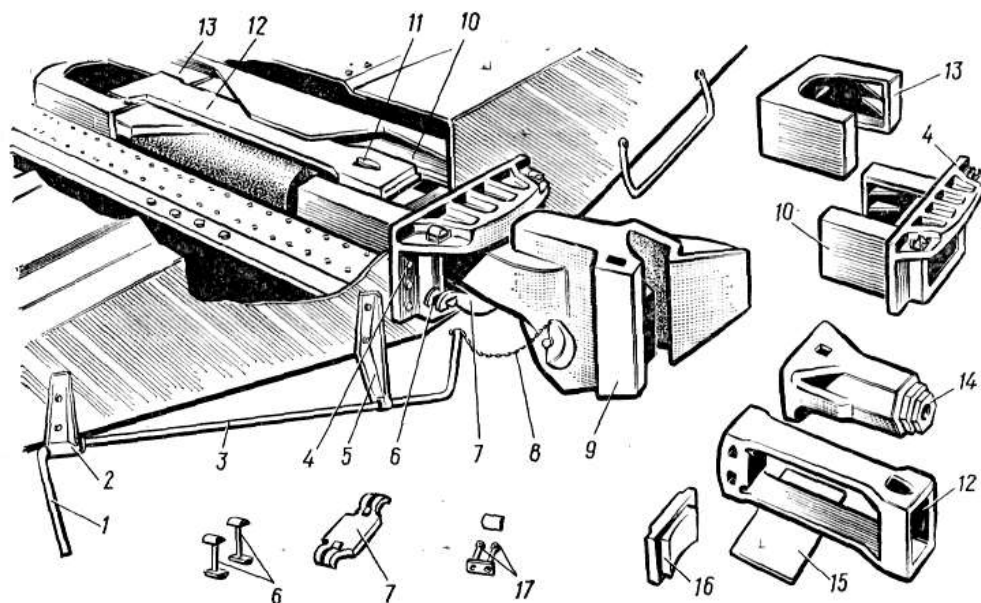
Розміщення деталей автозчепного пристрою вагонного типу
